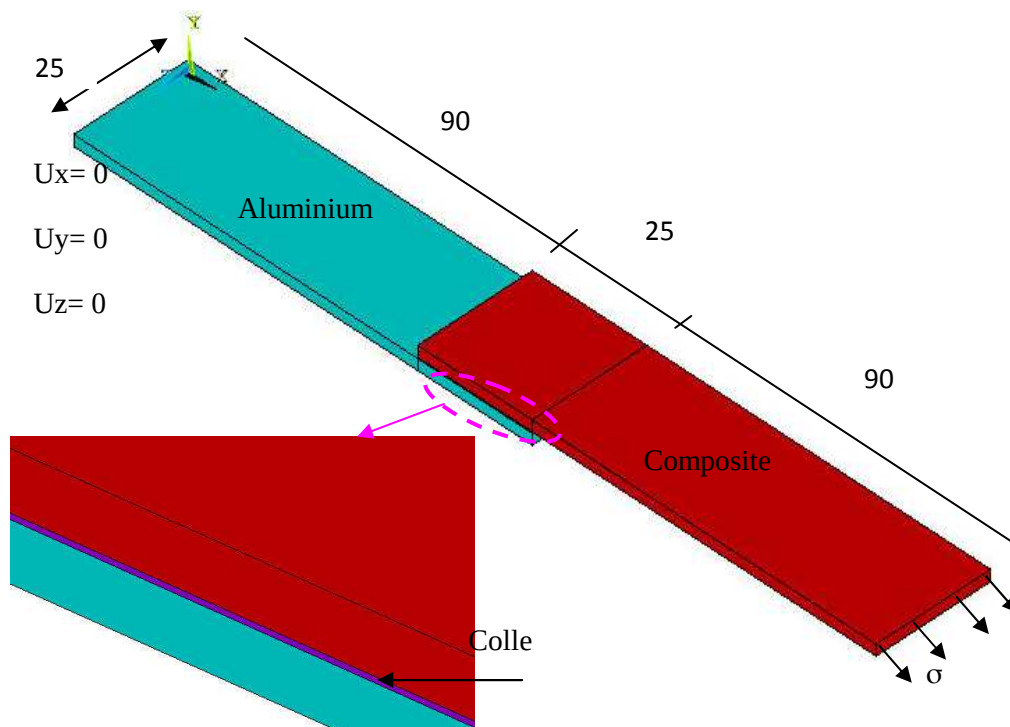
Géométrie de l'assemblage collé aluminium-composite
